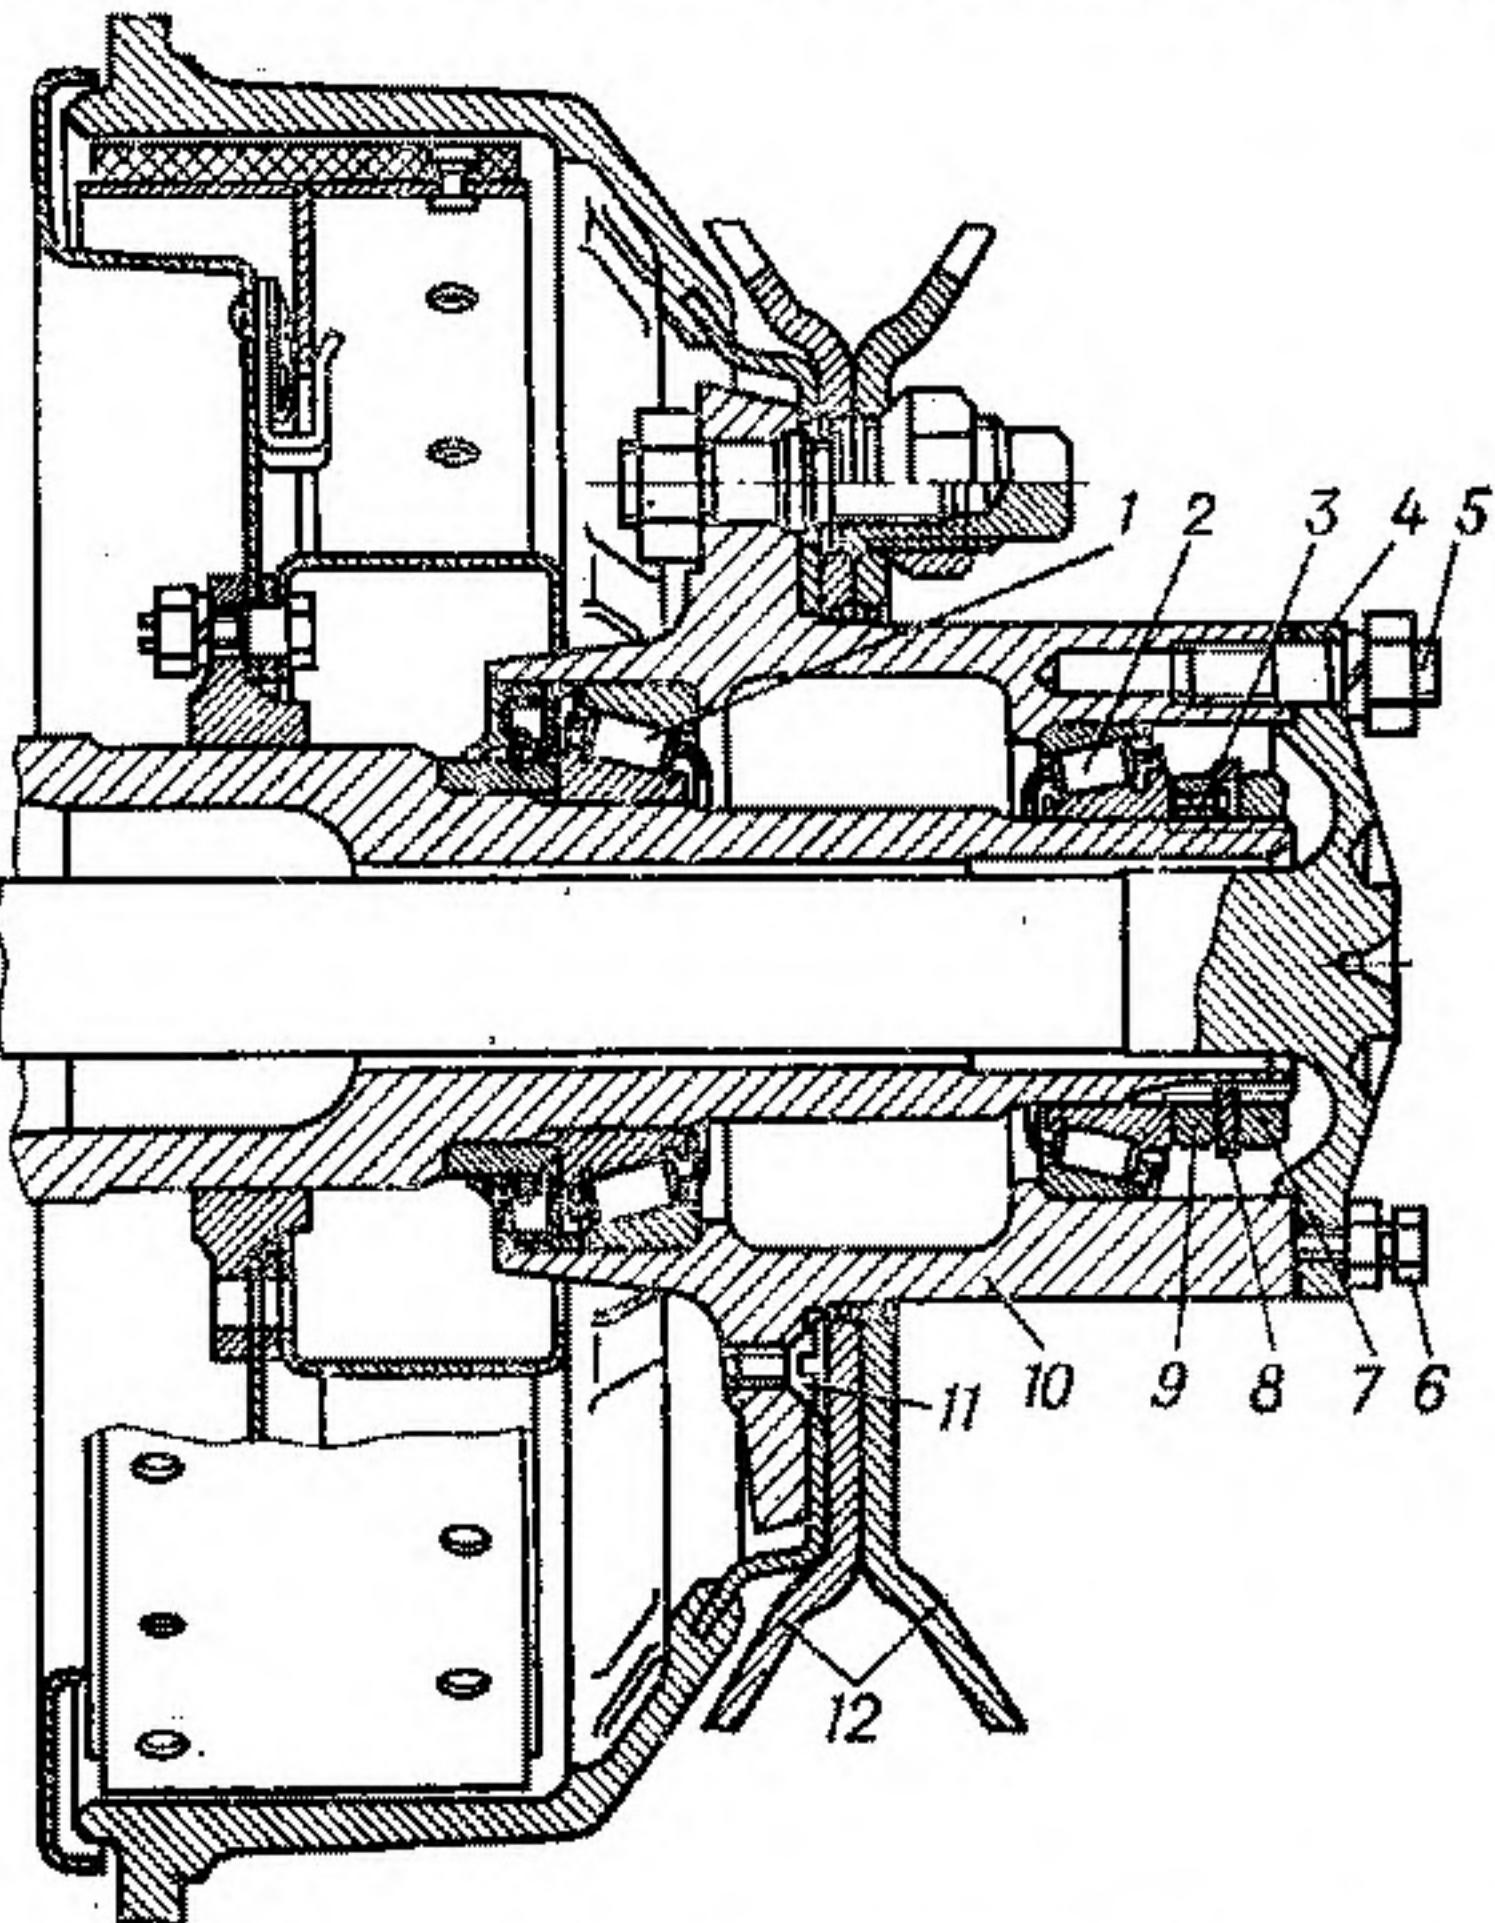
Ступица заднего колеса автомобиля ГАЗ-53-12:
